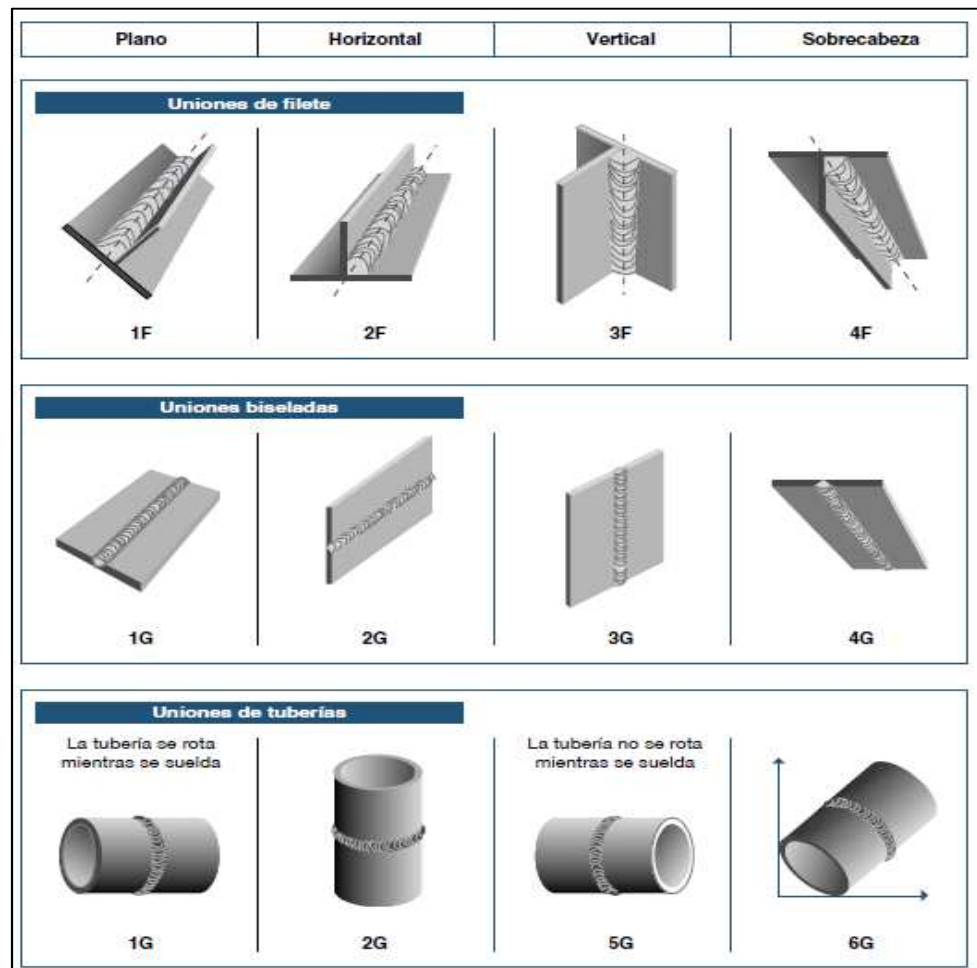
3 Posiciones de Soldadura (tomado de Indura)
